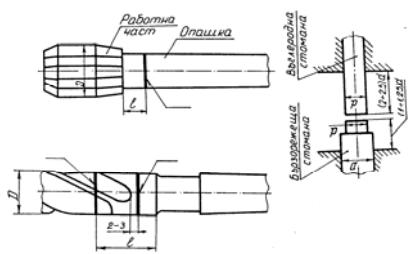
Монолитна металокерамична заготовка за свредло
